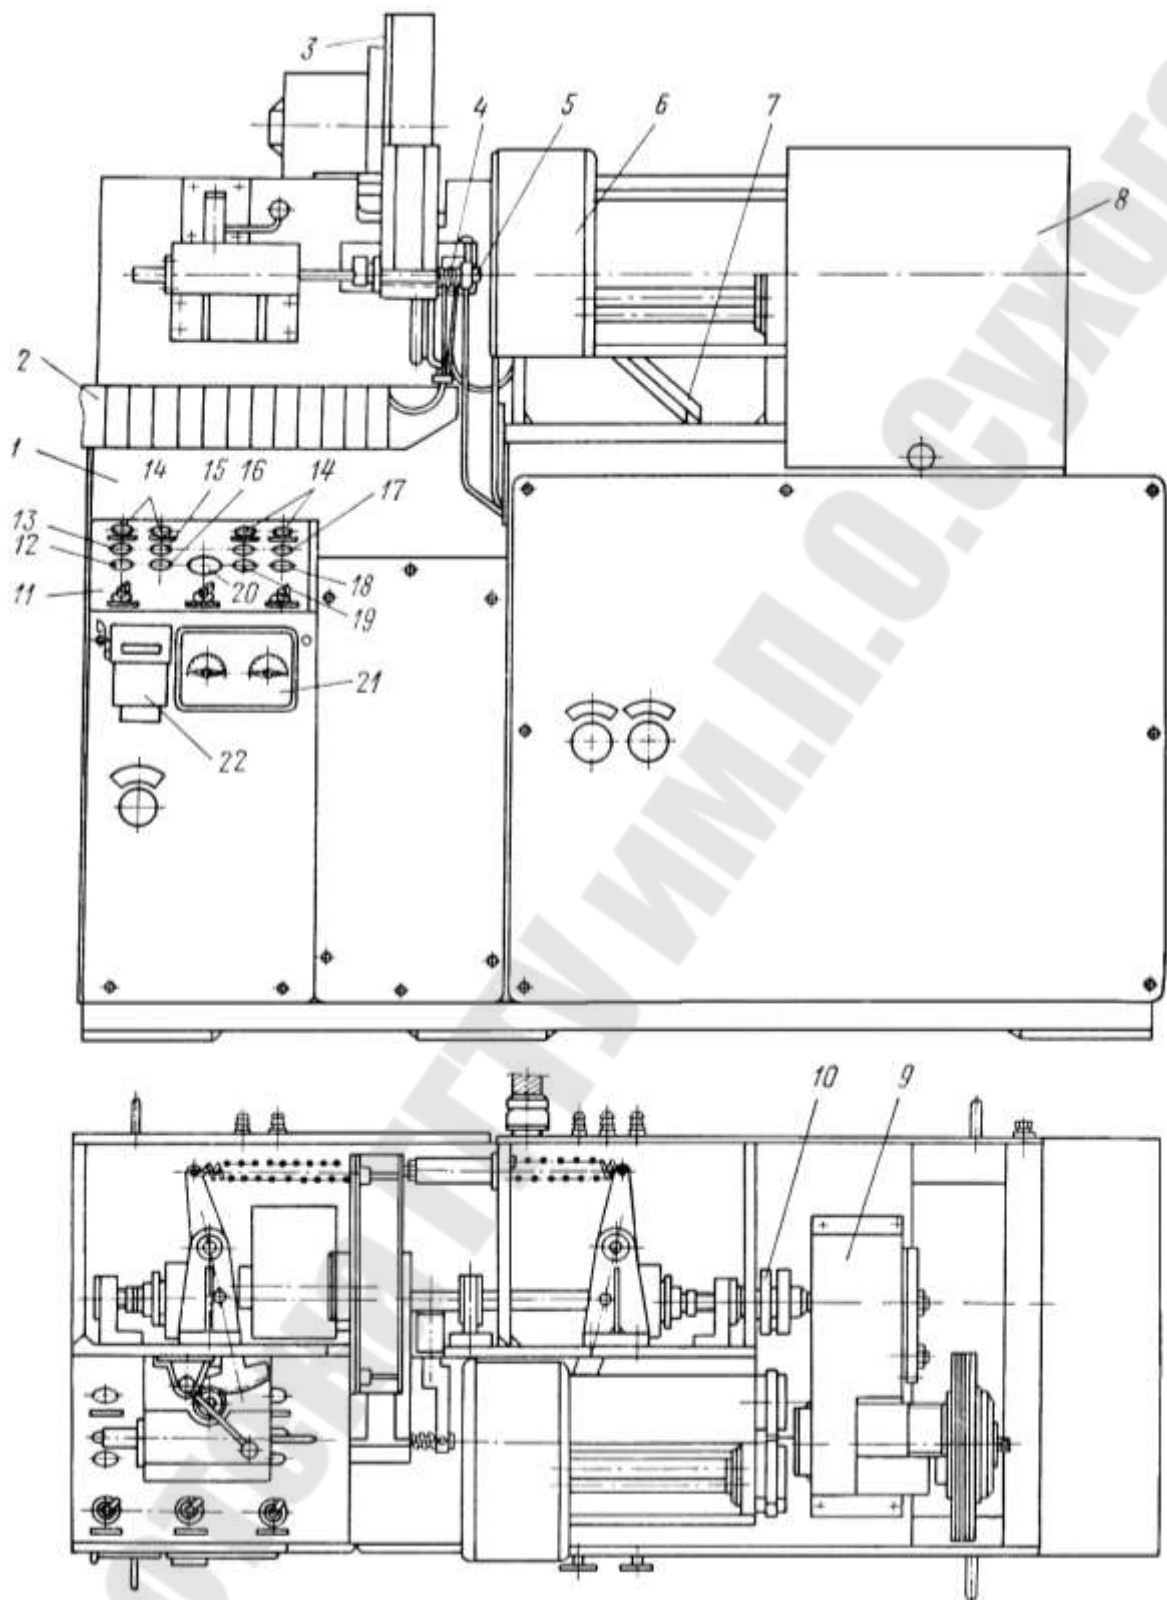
Эскиз общего вида стана для продольно-винтового проката сверл модели АСПС-3-5А: 1 – станина; 2 – токоподводящая шина; 3 – бункер; 4 – индуктор; 5 – передняя проводка; 6 – прокатная клеть; 7 – лоток отвода заготовок; 8, 9 – распределительные редукторы; 10 – распределительный вал; 11 – пульт управления; 12 – кнопка «Стоп» (общий); 13 – кнопка «Пуск»; 14 – сигнальная лампочка; 15 – кнопка «Пуск» электродвигателя; 16 – кнопка «Стоп» электродвигателя; 17 – кнопка «Пуск» нагрева; 18 – кнопка «Стоп» нагрева; 19 – наладочные кнопки; 20 – переключатель режима работы; 21 – реле времени; 22 – реле счета импульсов
